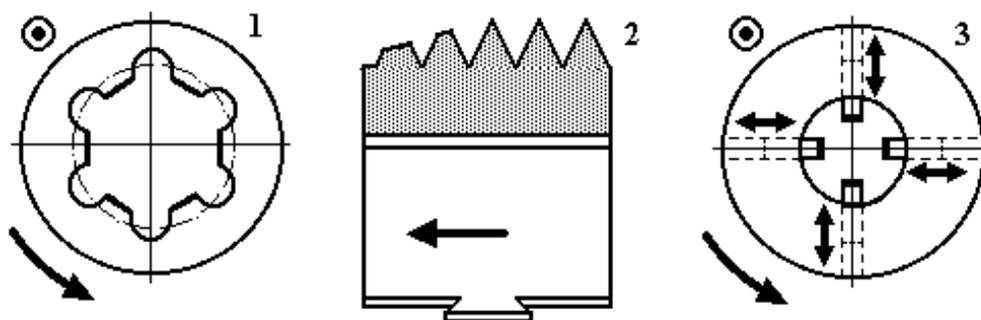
Резьбонарезные инструменты: 1 – круглая плашка; 2 – резьбовая гребенка; 3 – самораскрывающаяся резьбовая головка для нарезания наружной резьбы
